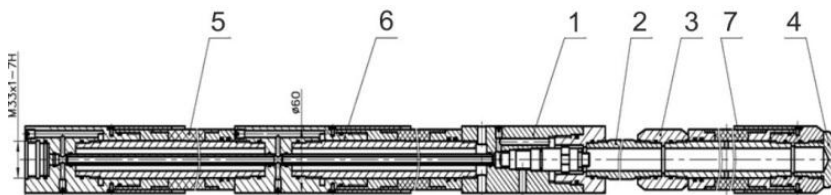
Общий вид устройства разрыва: 1 – инжектор, 2 – удлинитель, 3 – муфта удлинителя, 4 – заглушка, 5 – верхний пакер, 6 – инжекторный пакер, 7 – нижний пакер.
